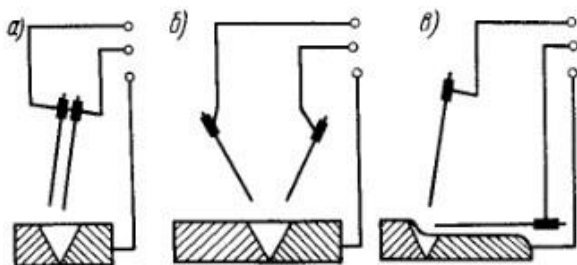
Схемы дуговой сварки трехфазной дугой [17]
